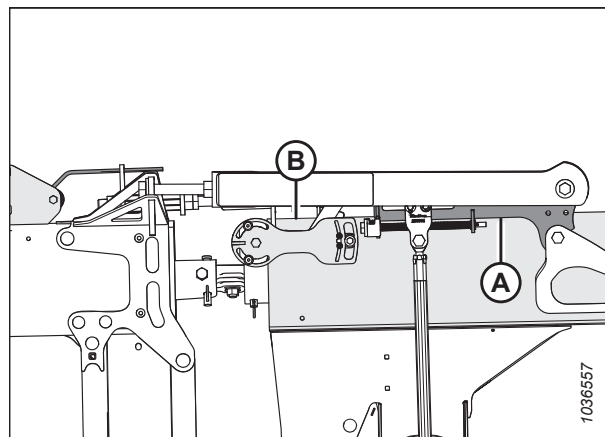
Bord inférieur du levier coudé parallèle au tube arrière
